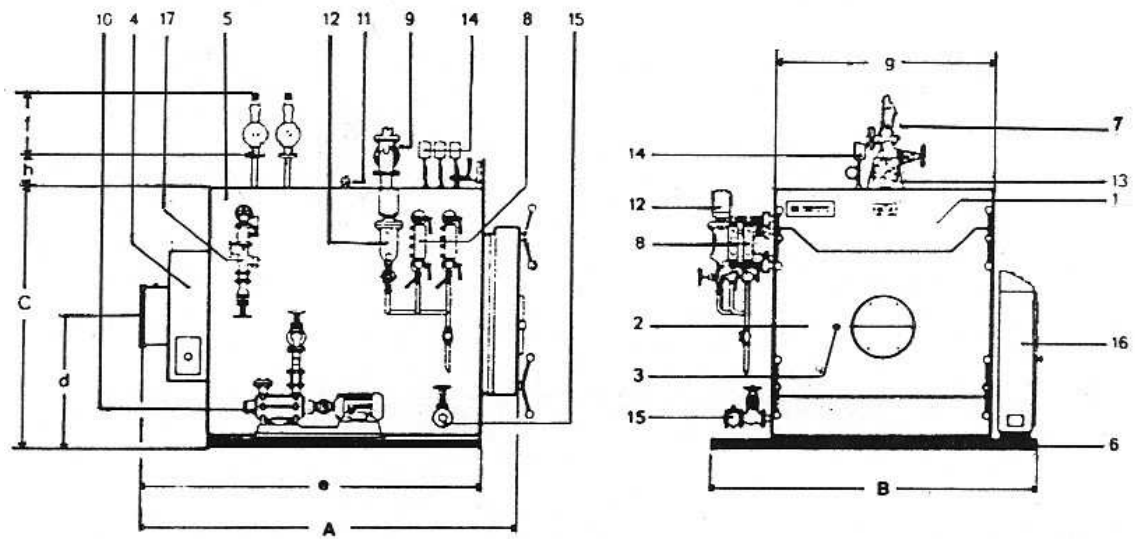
Componentes Principales de la Caldera PR 2 VM
